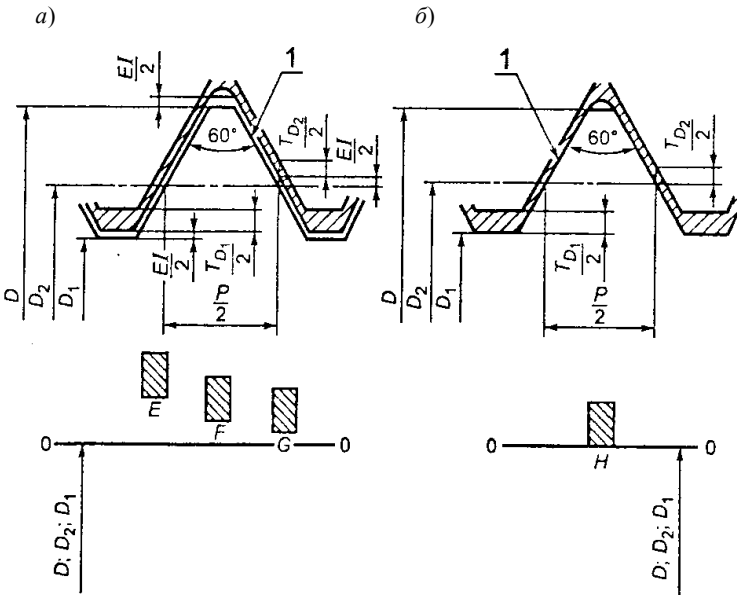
Положения полей допусков внутренней резьбы:
